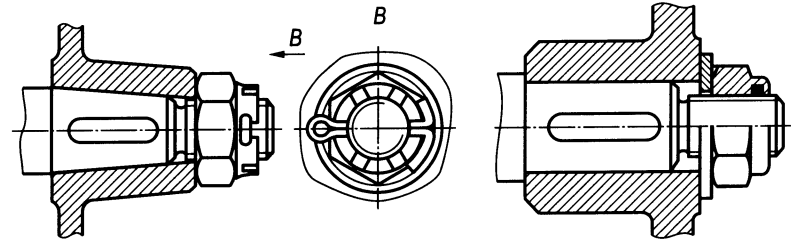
Крепление корончатой гайкой и шплинтом
